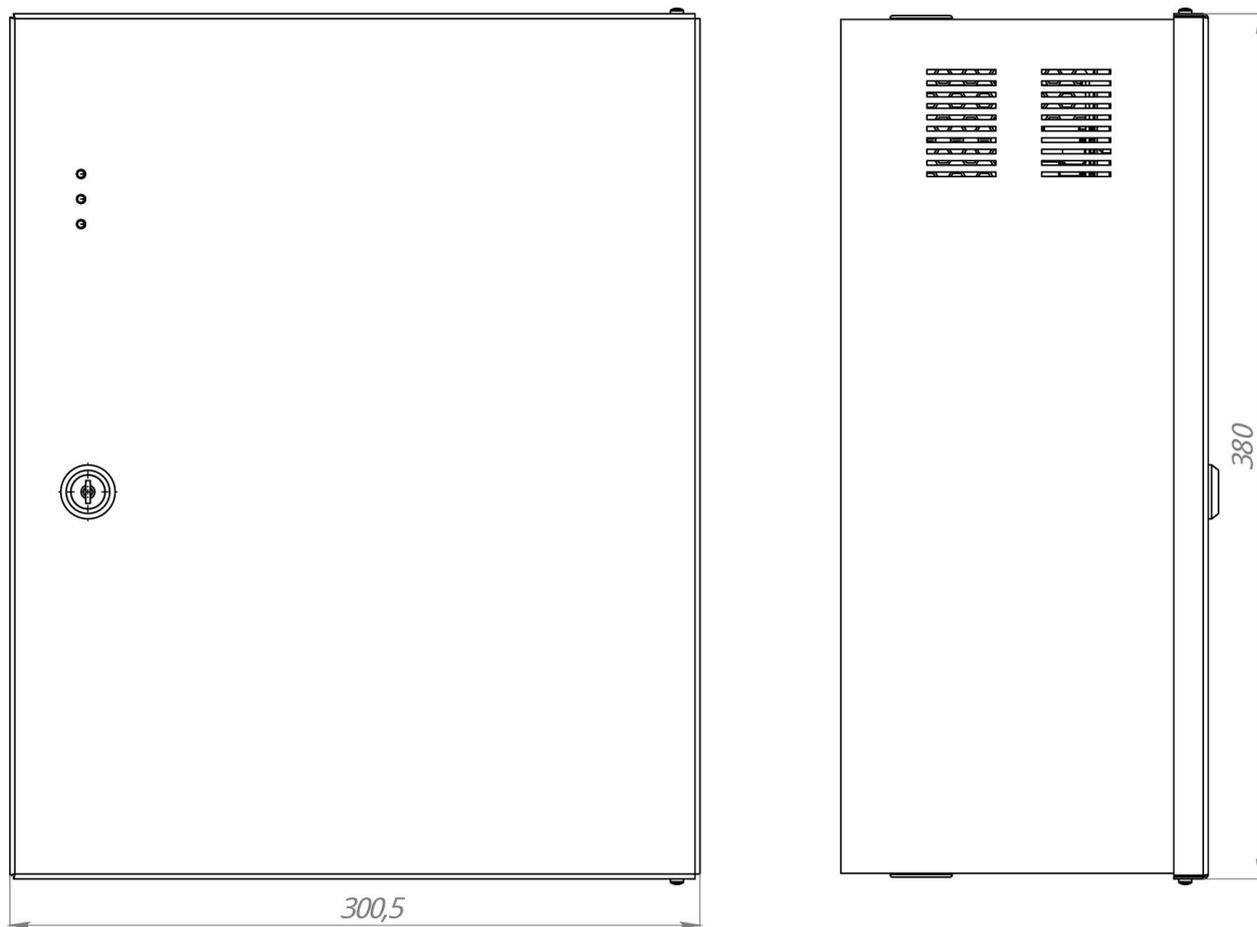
Габаритные и установочные размеры ПС16-МС
